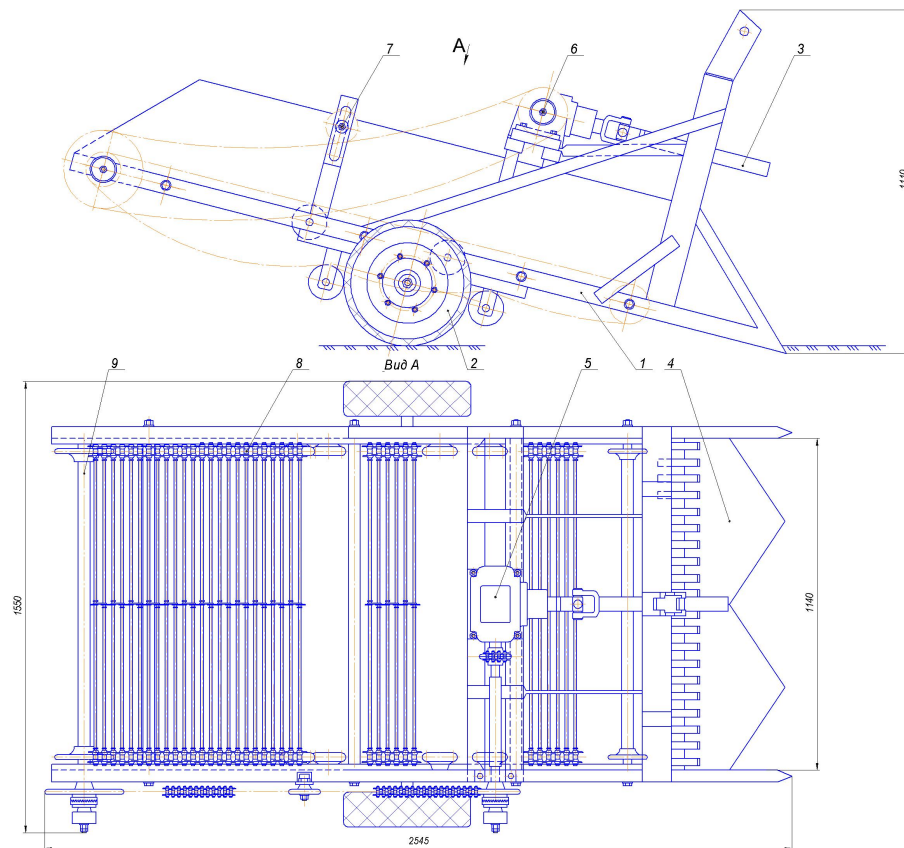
Схема розробленої картоплекопачки: 1 – рама; 2 – опорне колесо; 3 – карданна передача; 4 – лемеші; 5 – редуктор; 6 – ланцюгова передача вала приводу транспортера; 7 – натяжний пристрій; 8 – транспортер; 9 – ведуча зірочка транспортера; 10 – ведучий вал транспортера.
